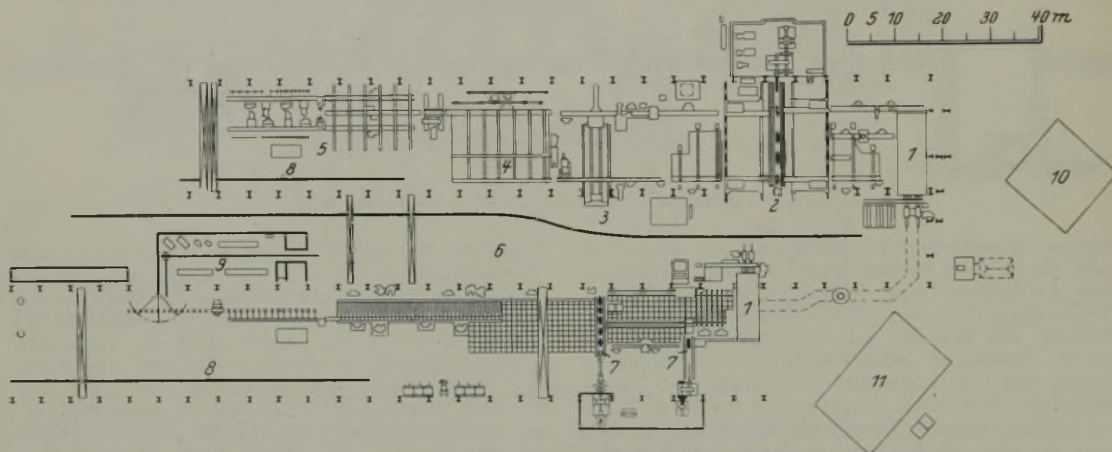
Lageplan der Walzwerke der Scullin Steel Co.
